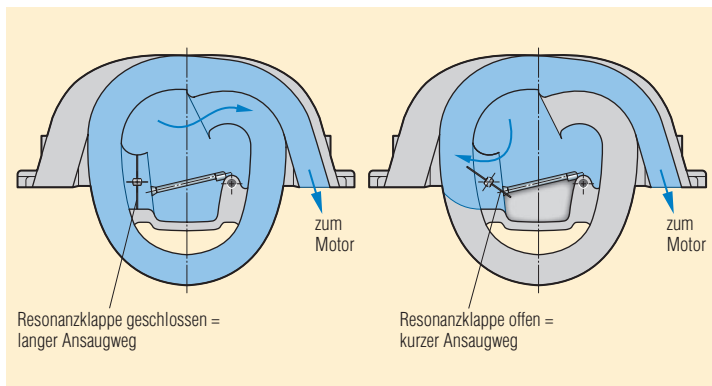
Schaltsaugrohr mit zwei Stufen.
